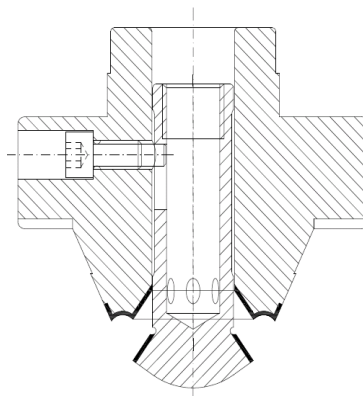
ZH se středovým ventilem (1-základní tělo ZH, 2-středový ventil)
